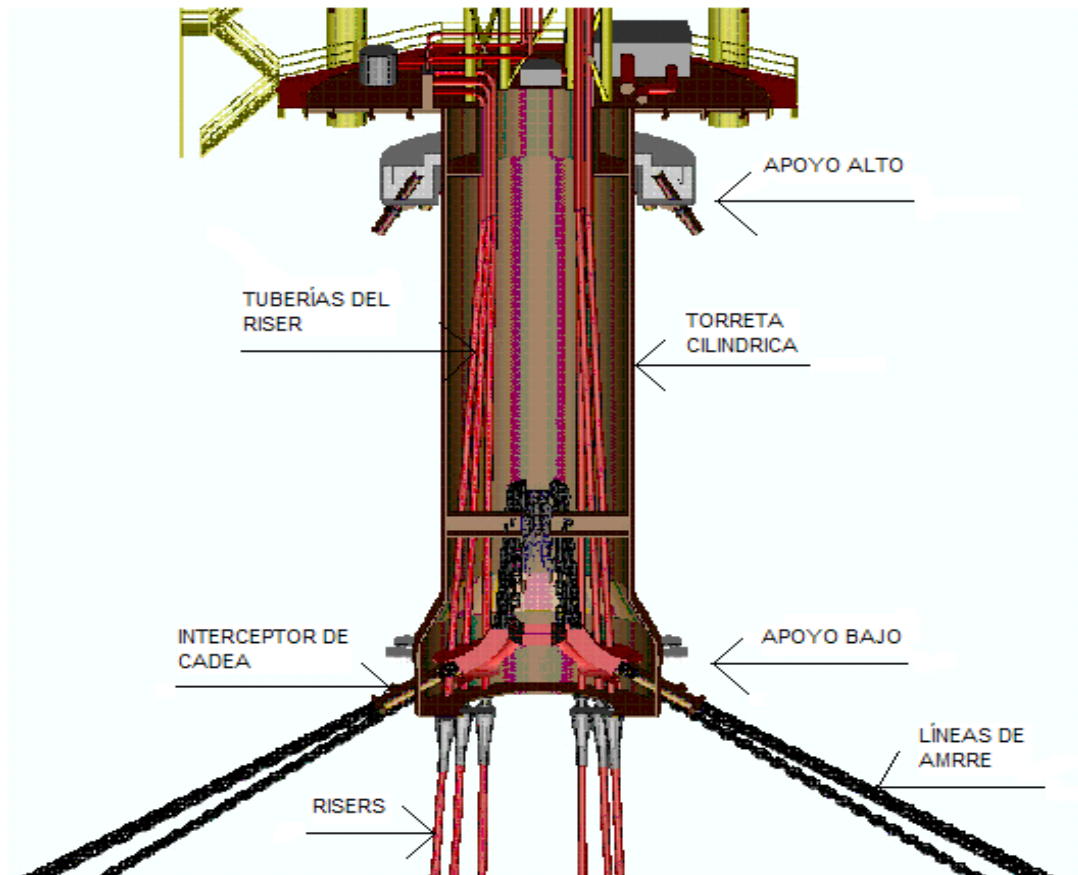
Componentes principales de una torreta (Fuente: [www.technip](http://www.technip.com), 2005).
